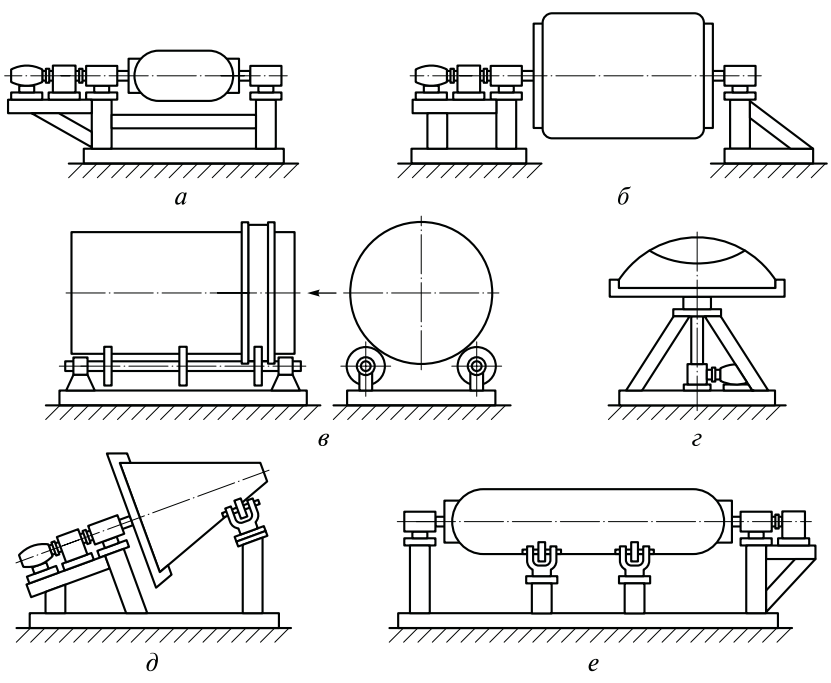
Схемы вращателей для сварки кольцевых швов:
